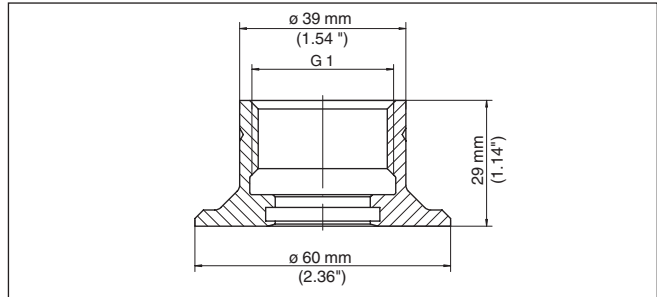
Maße Einschweißstutzen G1 (DIN 3852-A, ISO 228-1)
